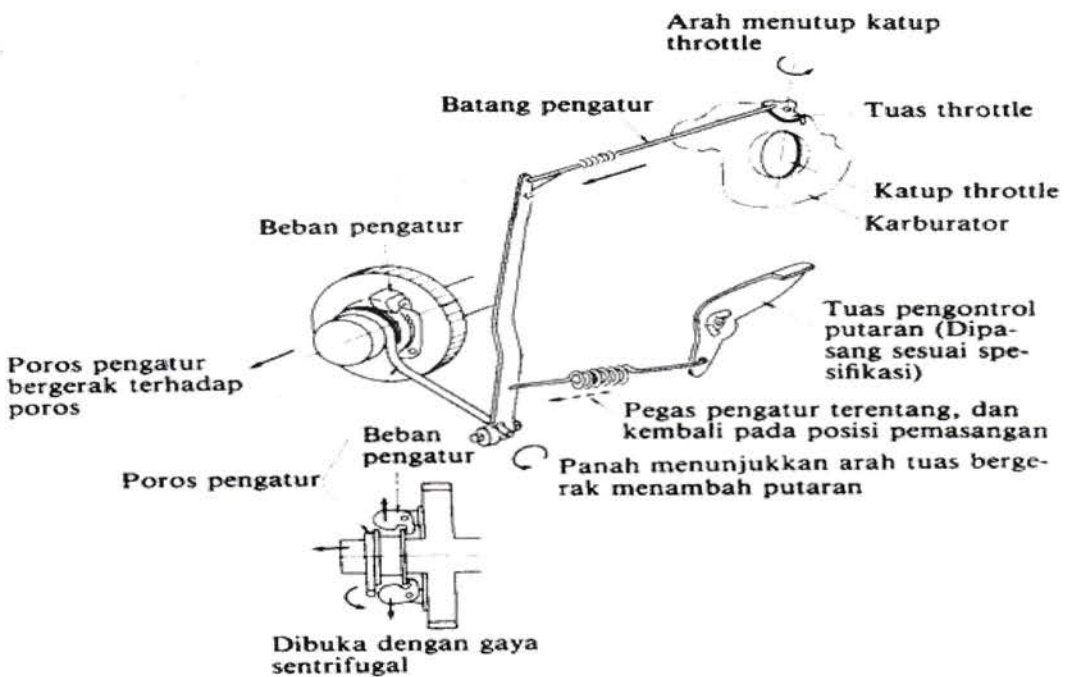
Detail Komponen suatu Karburator pada Motor Bensin
